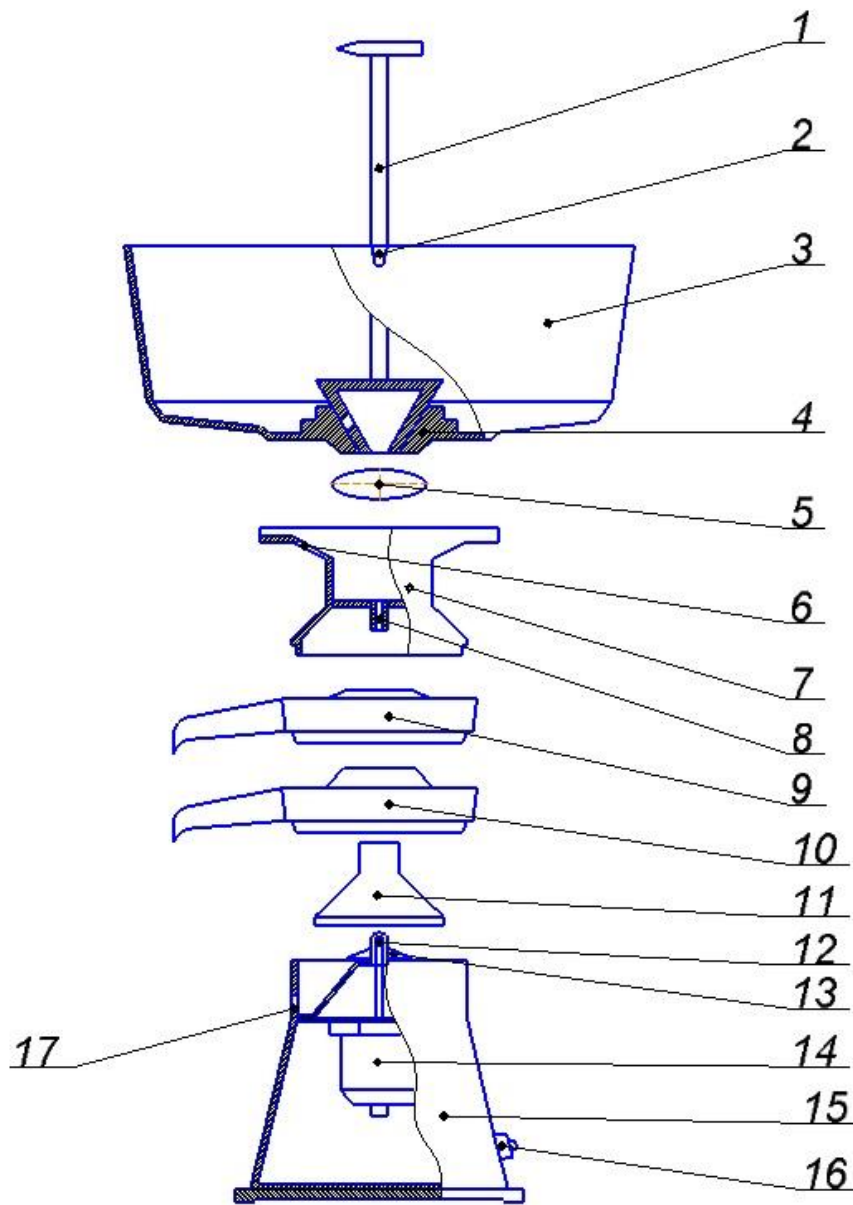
Устройство и схема сборки сепаратора-сливкоотделителя Сибирь-120-МЕТ-Р
